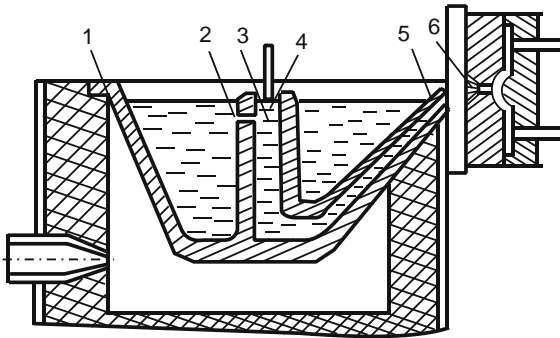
Схема поршневої машини гарячого тиску: 1 – ванна; 2 – рідкий метал; 3 – камера; 4 – поршень; 5 – ливник; 6 – прес-форма
